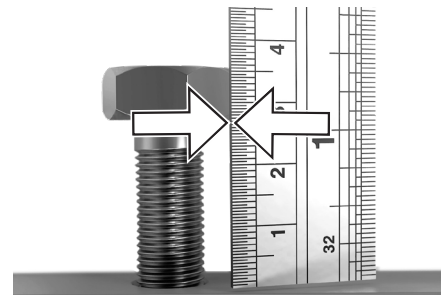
B – Schraube auf die gewünschte Schnitthöhe einstellen und Mutter festziehen (im obigen Beispiel auf 27 mm eingestellt)
